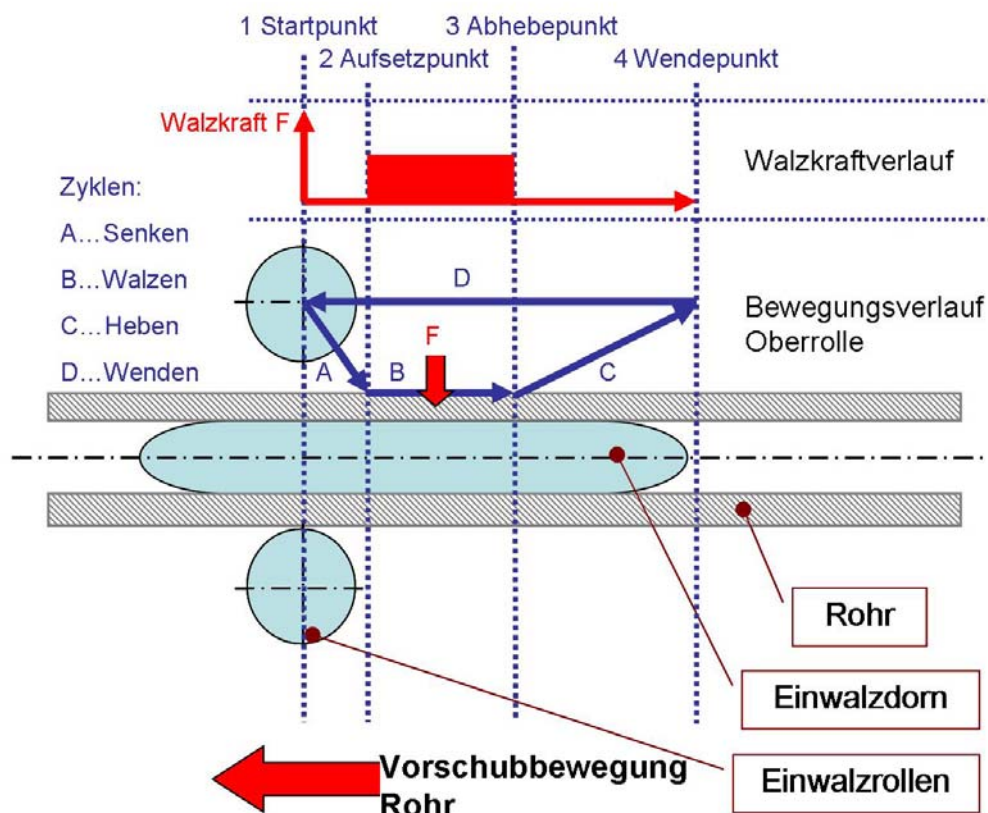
Funktionsprinzip Nahteinwalzung zyklisch vertikal und horizontal bewegte Oberrolle
